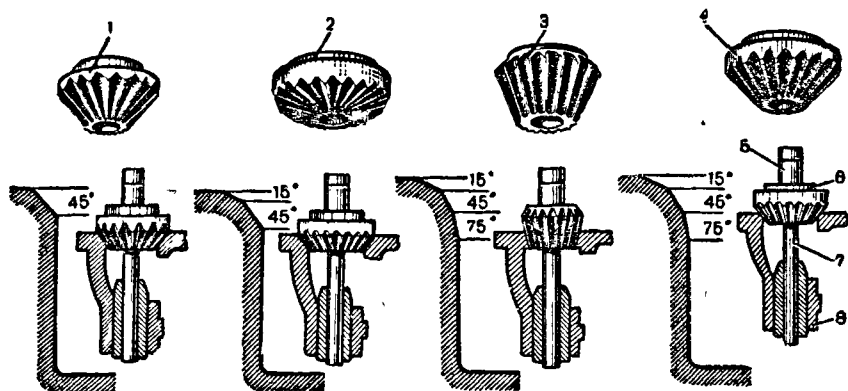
Схема обработки седла клапана: 1—4 — шарошки; 5 — оправка для крепления шарошек; 6 — седло клапана; 7 — направляющая оправка; 8 — втулка клапана
